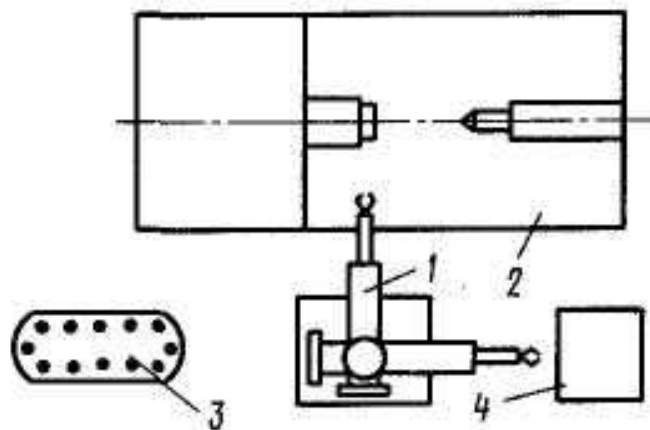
Компоновка верстатного комплексу на базі токарного багаторізцевого верстата 1А730Ц
